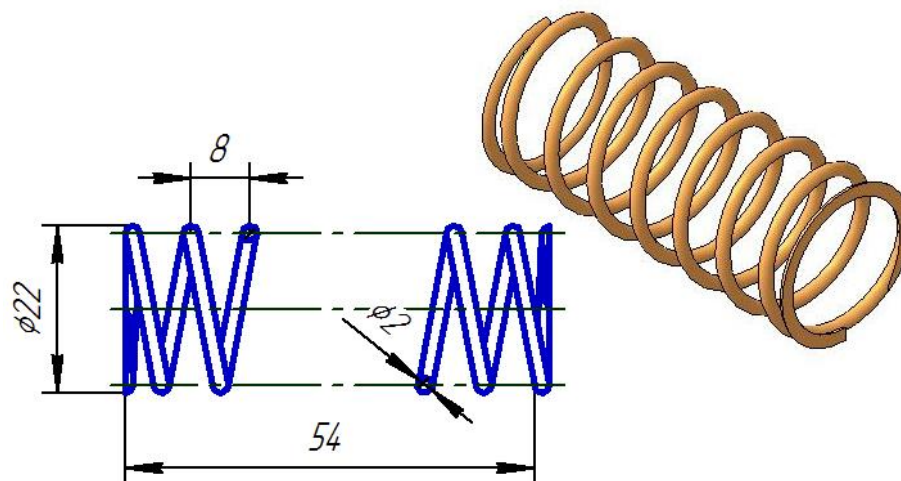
Чертеж и модель детали «Пружина сжатия»
